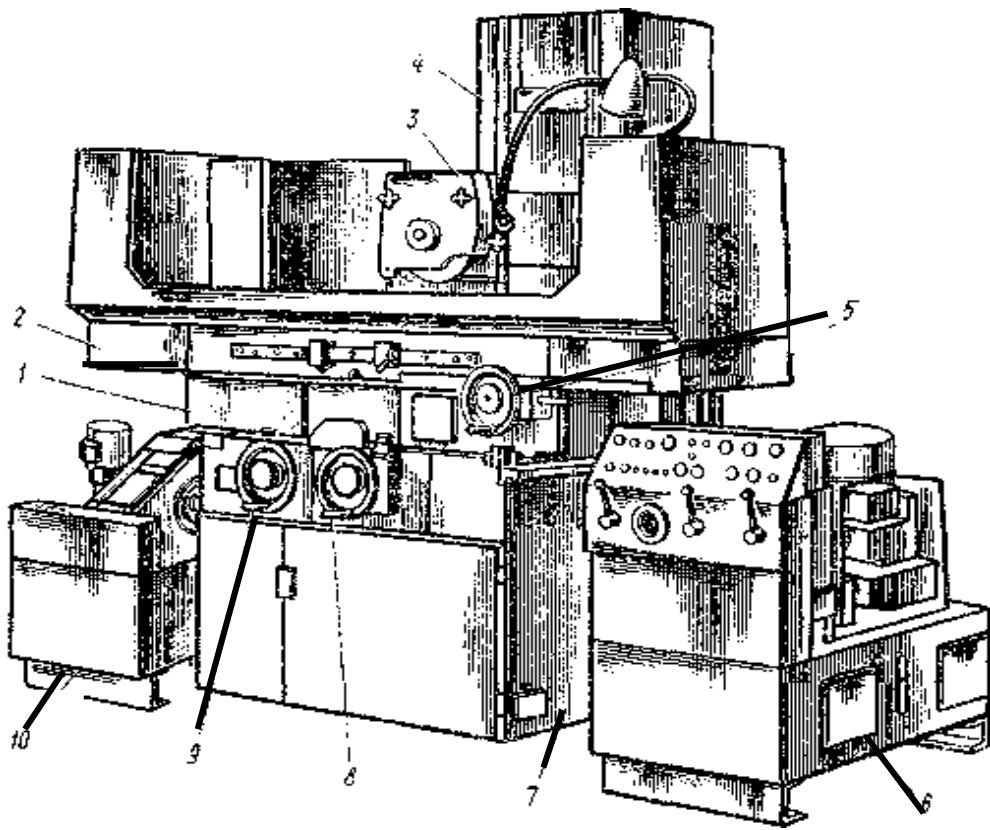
Внешний вид плоскошлифовального станка модели ЗЕ721ВФ1-1
